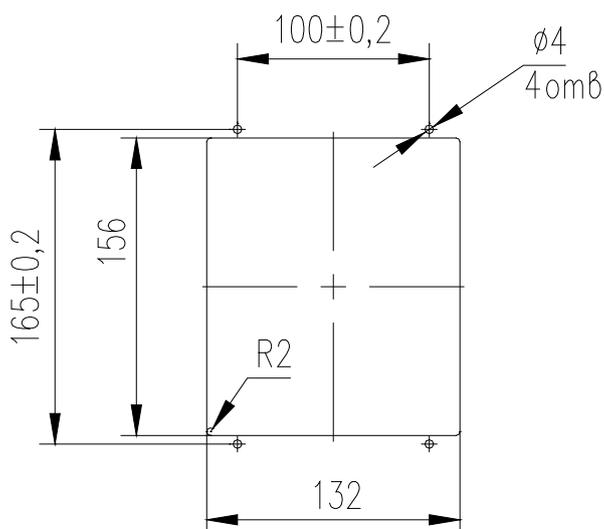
Размеры окна для монтажа БОИ в приборном щите.
